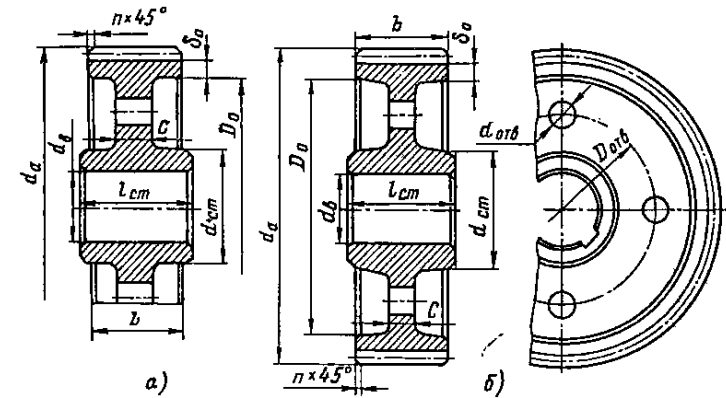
Цилиндрические зубчатые колеса при $d_a \leq 500$ мм
